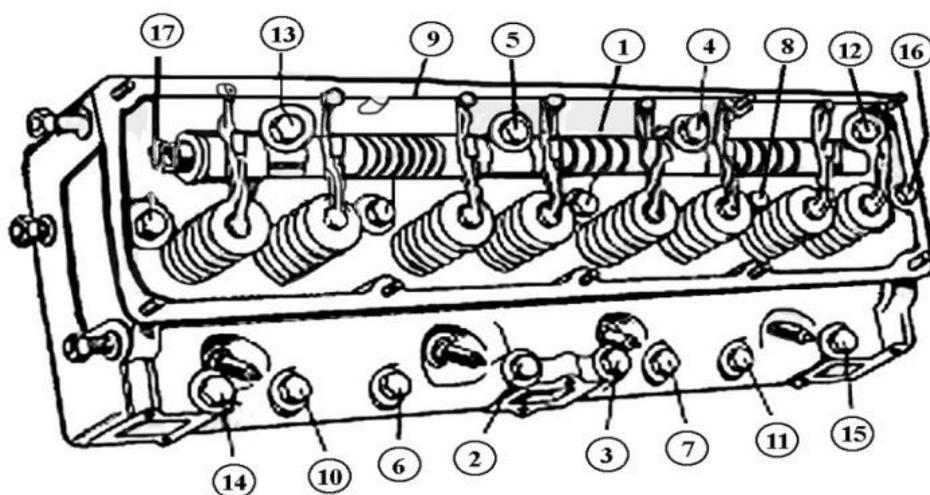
Порядок затяжки болтов крепления головки блока цилиндров двигателя ЗИЛ-508.1
